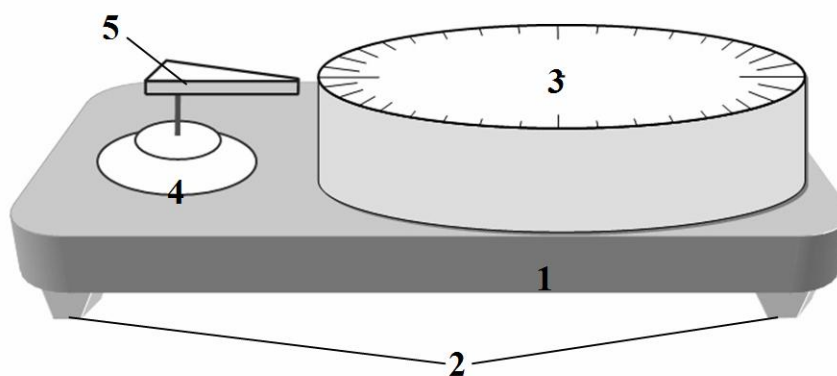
Схема ручного поворотного столика (общий вид):
